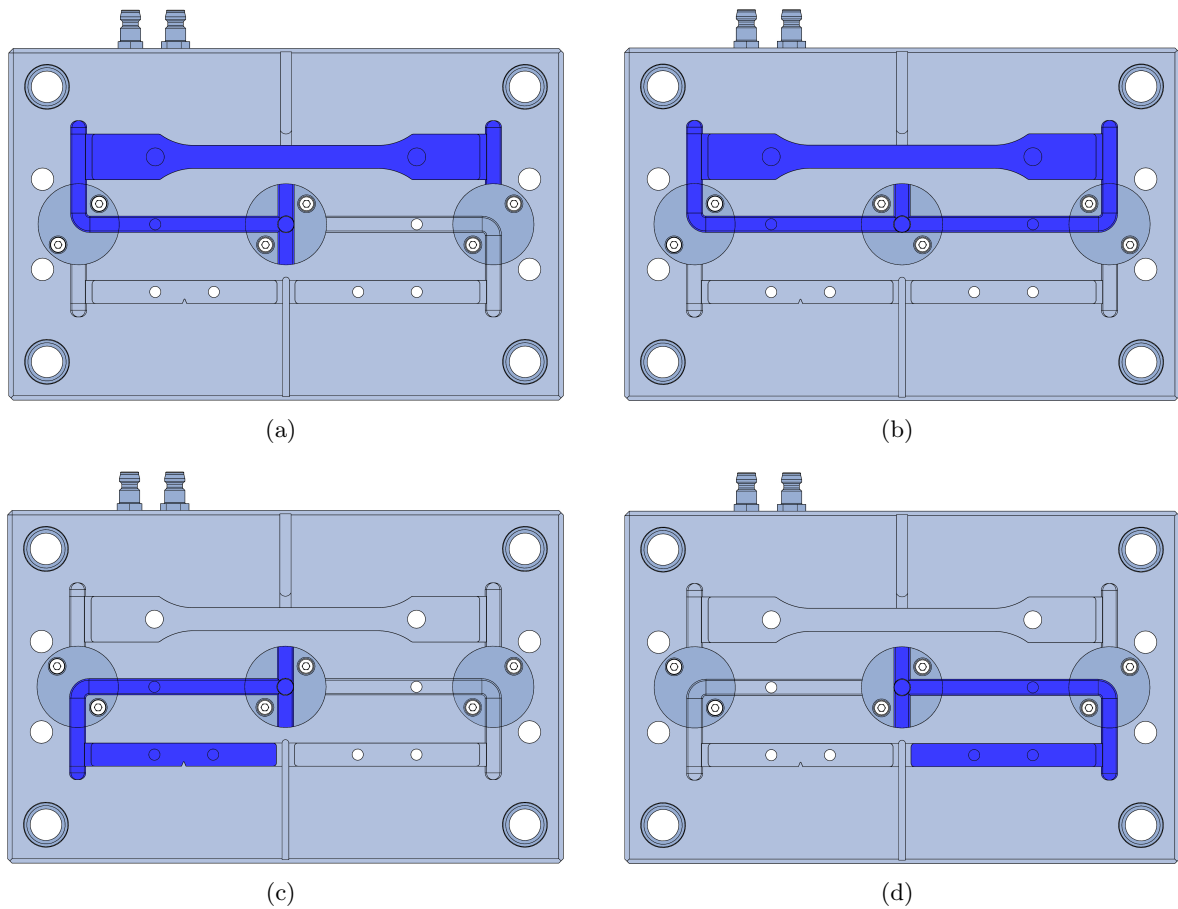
Moldação do provete de: (a) tração, (b) tração com linha de soldadura, (c) impacto com entalhe e d) impacto sem entalhe ou flexão.
